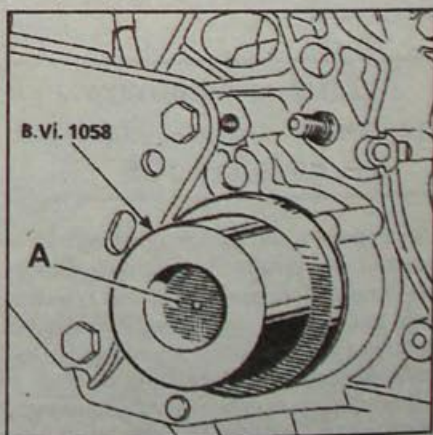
Использование оправки B. Vi. 1058 и защитного колпачка (A) оправки B. Vi. 945 для установки сальника правого приводного вала коробки передач JC5
